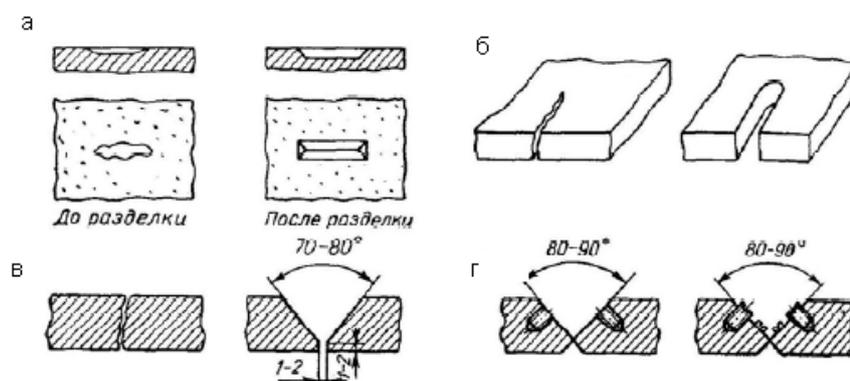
Схема подготовки дефекта к сварке:
